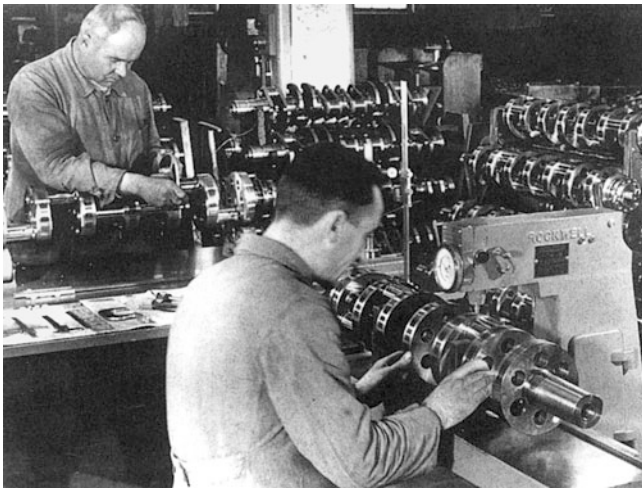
Montieren der Gegengewichte und Auswuchten der Scheibenkurbelwellen für MD- und GTO-Motoren
